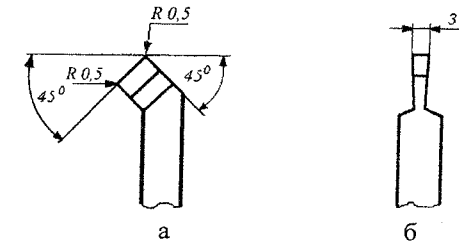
Схемы резцов: а – резец токарный проходной с отогнутой головкой и пластиной из твердого сплава Т15К6; б – резец токарный отрезной с пластиной из твердого сплава Т15К6
